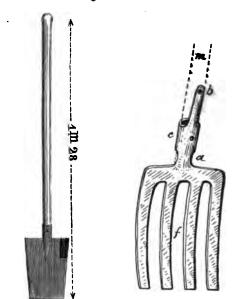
Bêche avec Fig. 173. — Assemblage assemblage à douille.
